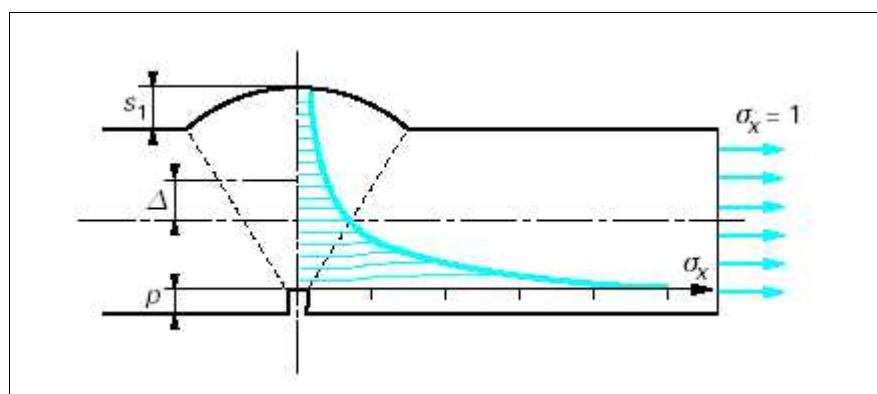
Défaut plan débouchant en racine sur un assemblage dissymétrique
